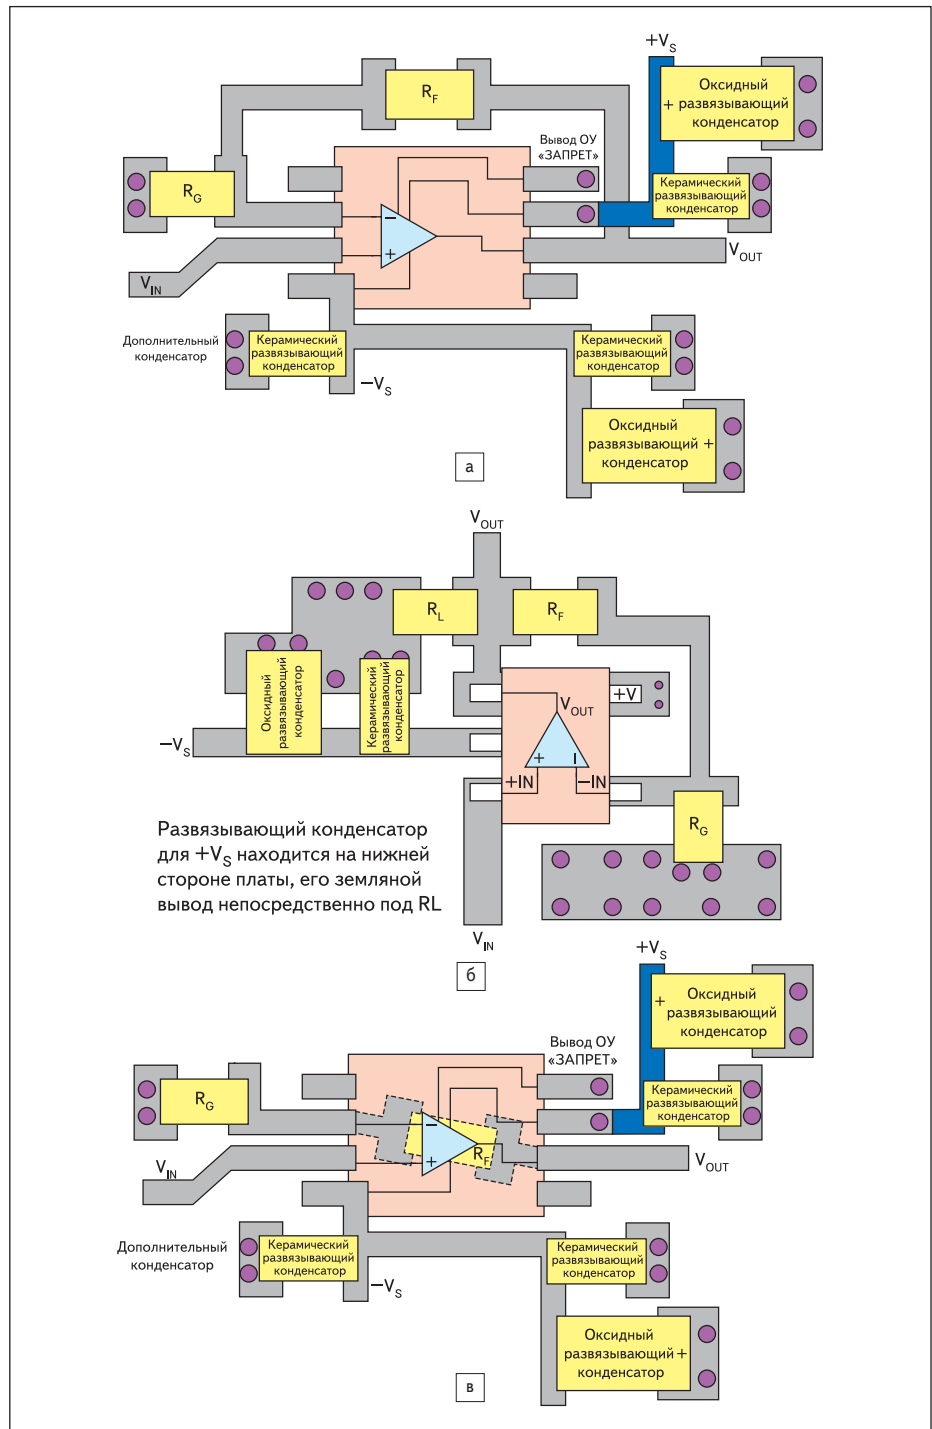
Отличия топологии схем с ОУ: а) корпус SOIC; б) корпус SOT-23; в) корпус SOIC с резистором R_F с нижней стороны платы
